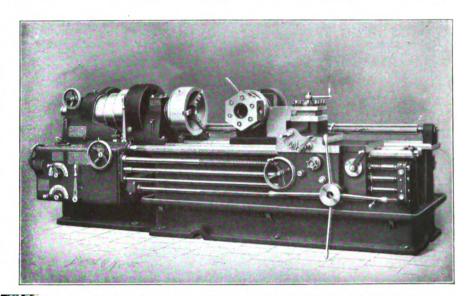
Revolverdrehbank mit Doppelbett der Magdeburger Werkzeugmaschinenfabrik G. m. b. H.
